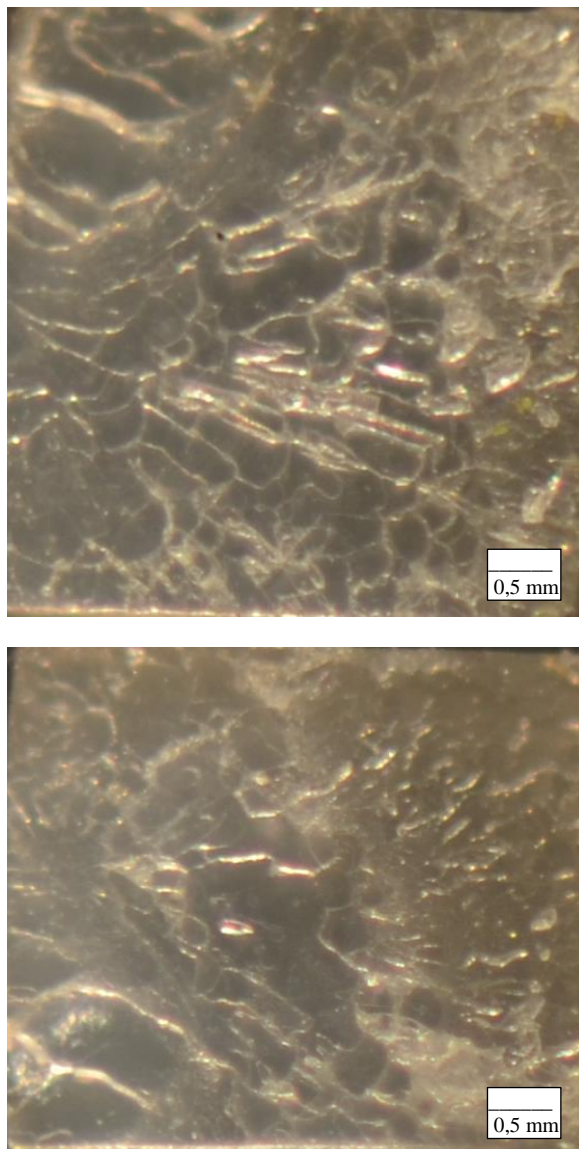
Aspecto da fratura dos corpos de prova injetados no inserto VRE, à temperatura de 210 °C e comprimento de fluxo 1, (a) com linha de solda e (b) sem linha de solda.
